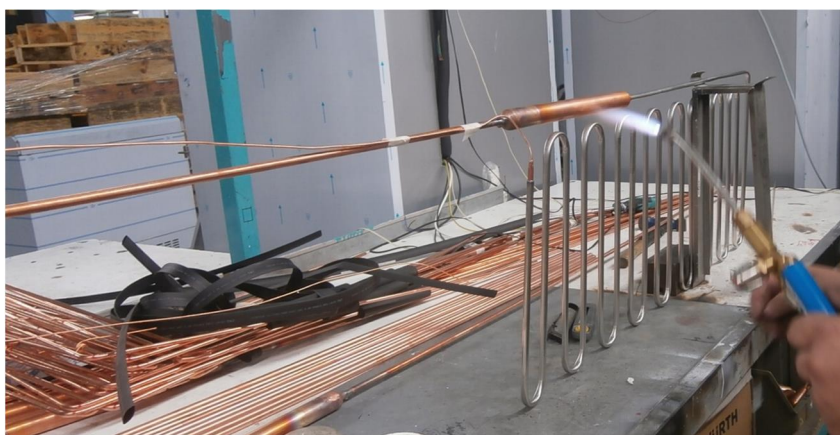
Operação de soldadura na serpentina de inox
